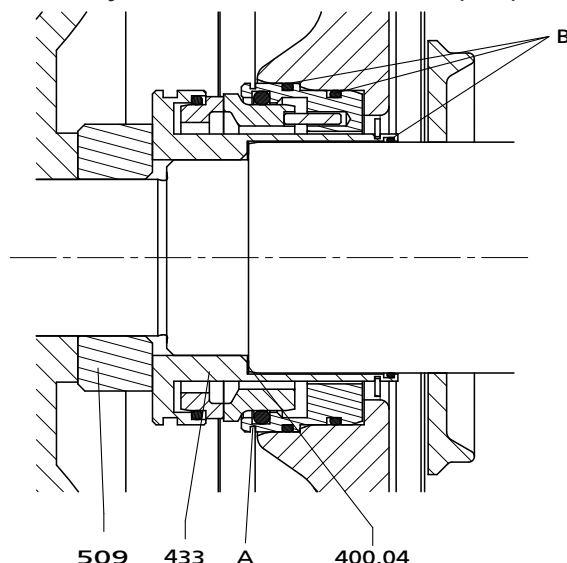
Монтаж уплотнительного блока KSB (4EB)
